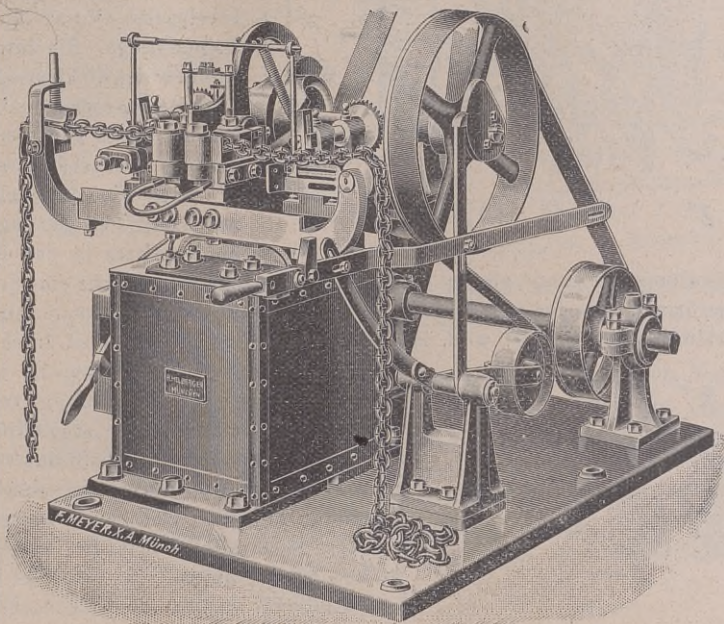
Elektrische Kettenschweißmaschine Type II für Glieder von 5–6 und 7 mm Stärke 15 Glieder pro Minute.
